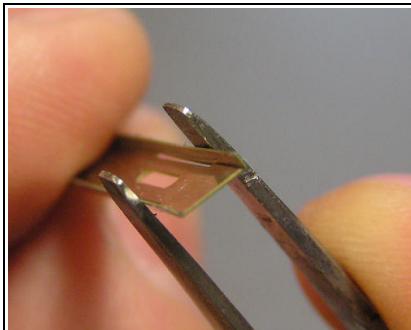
Die Seitenkanten mit der Flachzange oder Pinzette in mehreren Schritten über die gesamte Länge bis zu 90° biegen.
